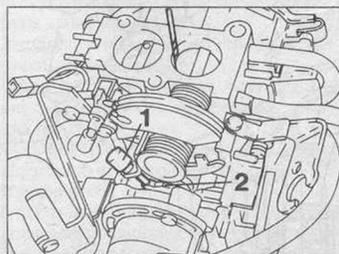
Проверка зазора дроссельного клапана (Глава 16)
